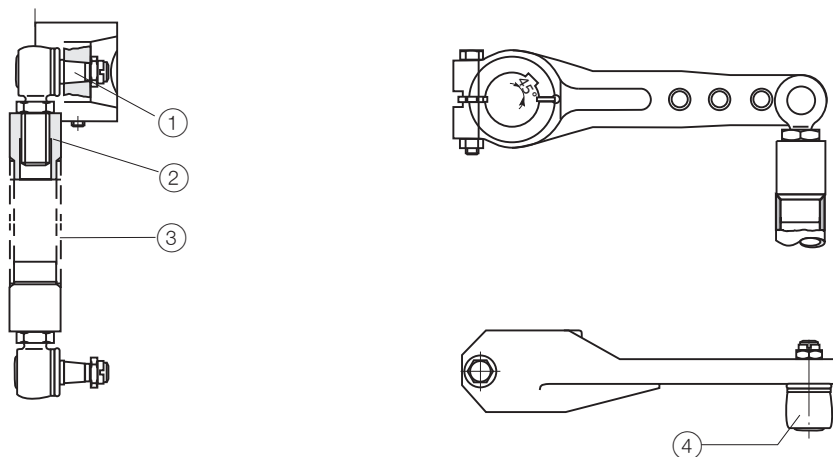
Компоненты соединительной тяги и размеры соединительной трубки
